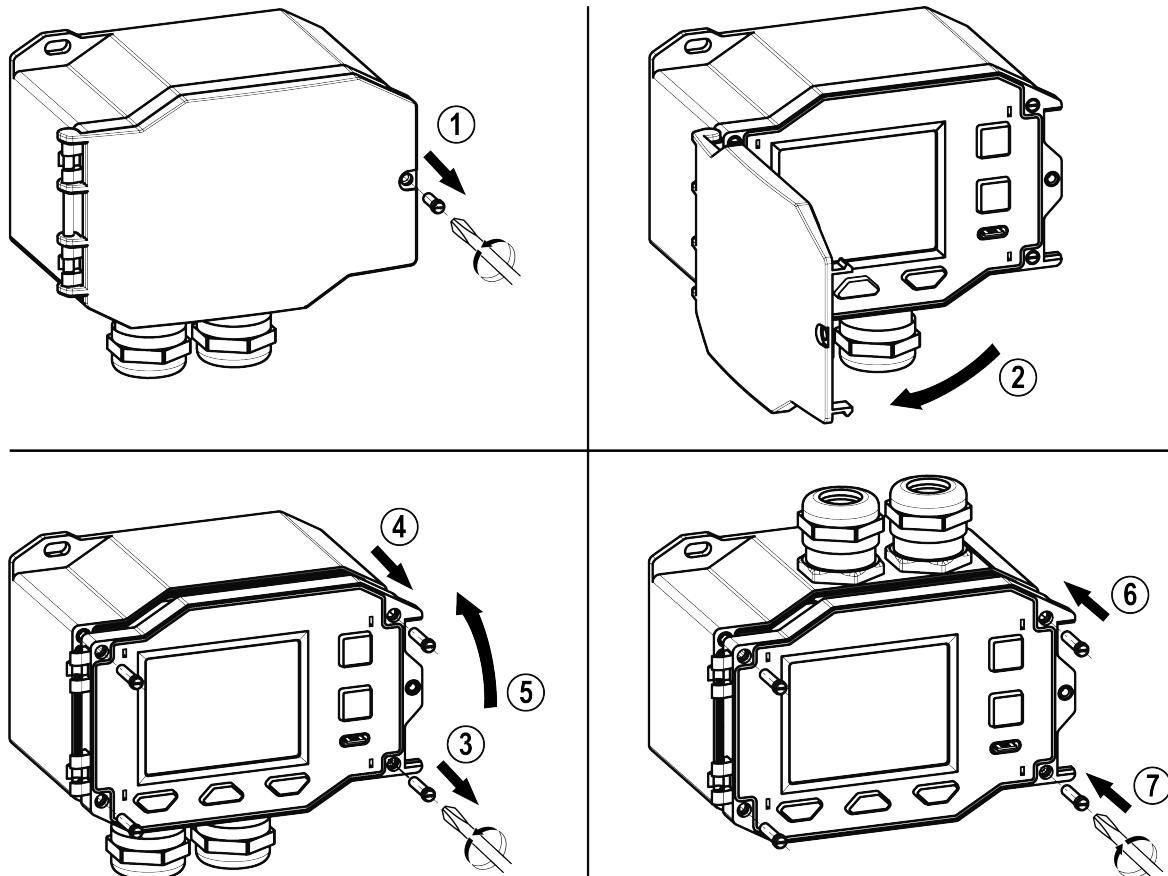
Поворот корпуса САУ-У2-Н4
